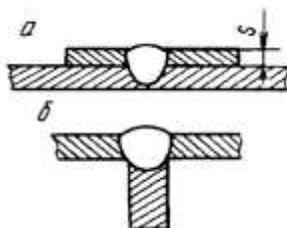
Проплавные швы: а – нахлесточного соединения; б – таврового соединения; s – толщина проплавляемой детали
